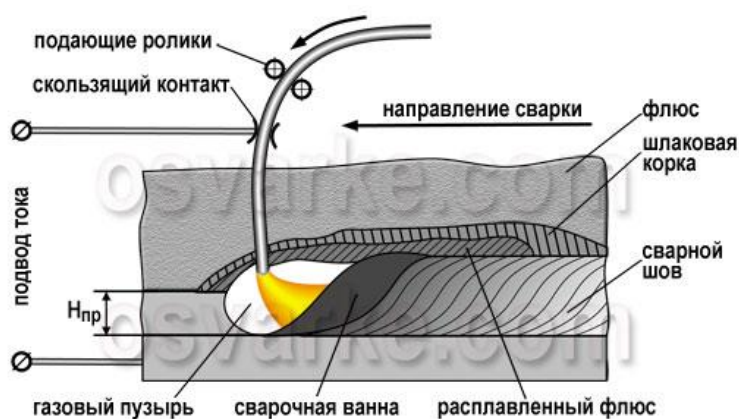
Схема выполнения сварки под флюсом
